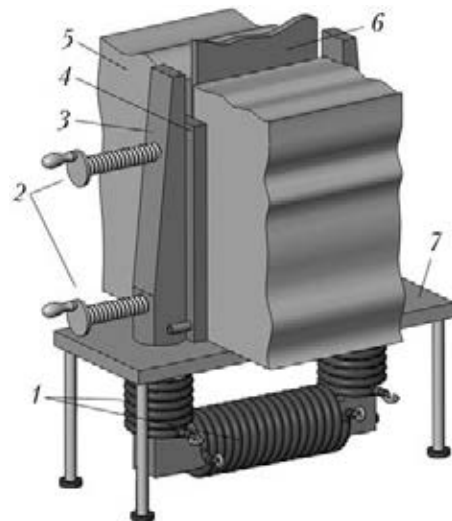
Устройство для электрошлаковой сварки во внешнем магнитном поле: 1 — катушки; 2 — прижимы; 3 — магнитопровод; 4 — водоохлаждаемая формирующая планка; 5 — свариваемый образец; 6 — электрод; 7 — опора
